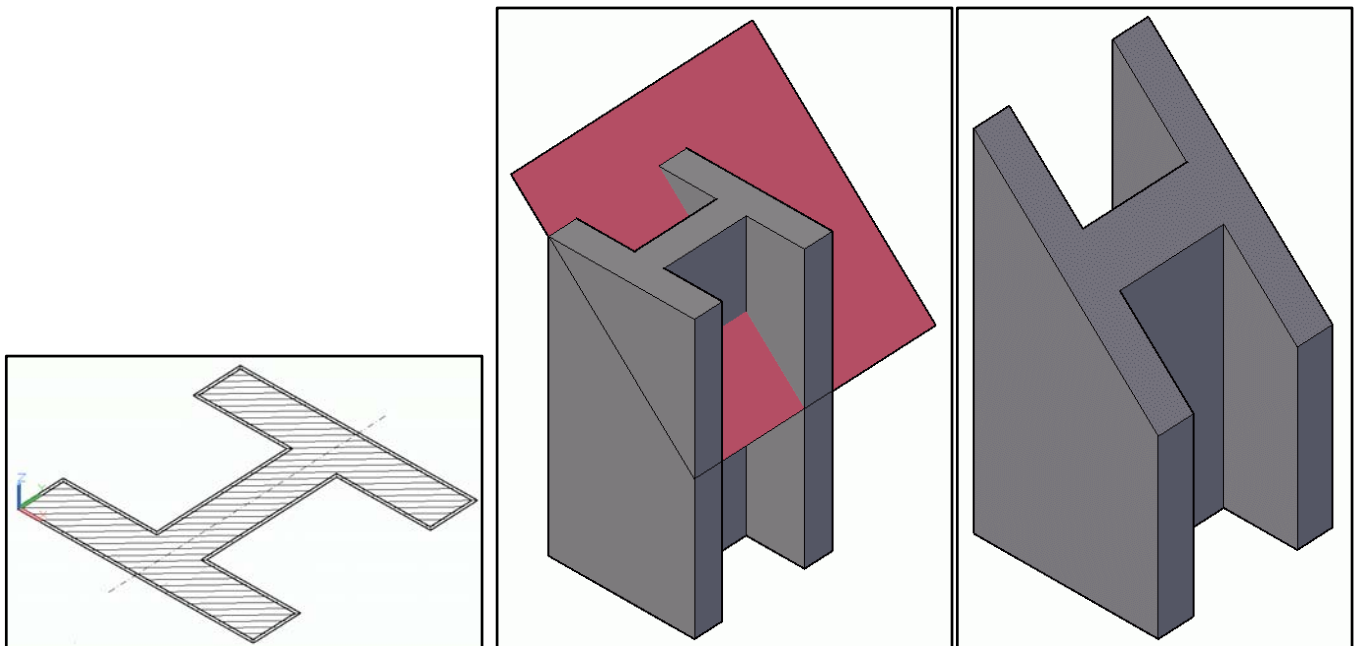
Profil (links) – Extrusion mit Schnittrechteck (Mitte) – ebener Schnitt (rechts)
